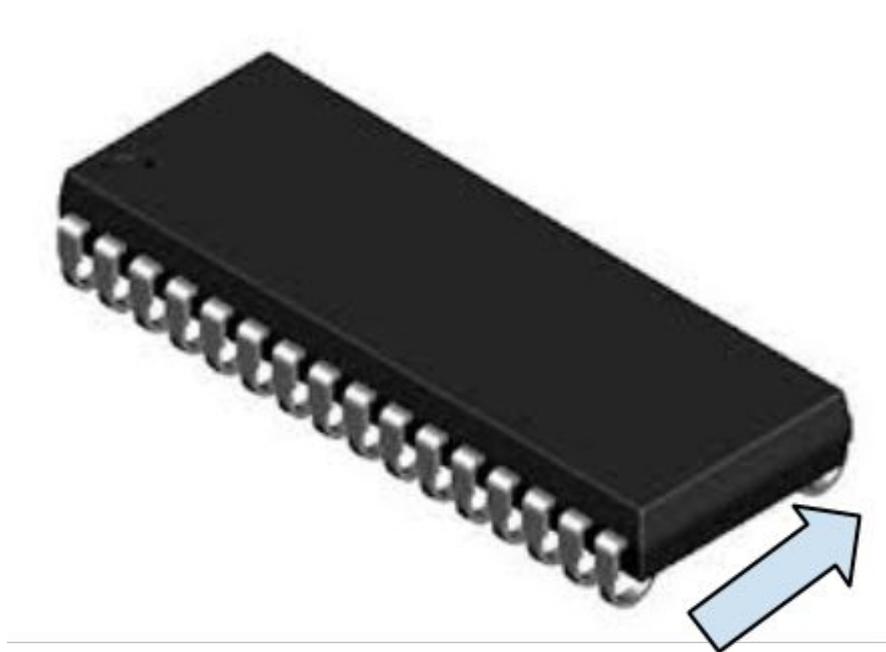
Dirección que puede causar soldaduras por ola defectuosas.
